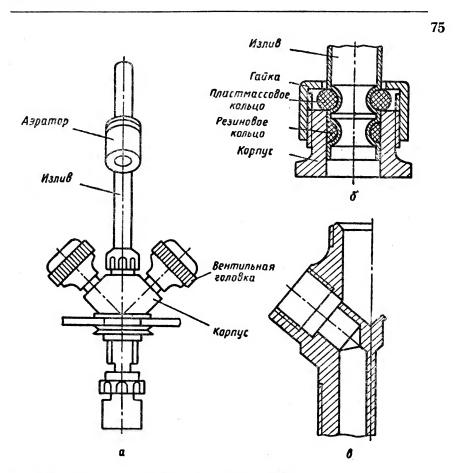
Смеситель для умывальника центральный: а — общий вид смесителя; б — узел излива; в — разрез корпуса смесителя.
